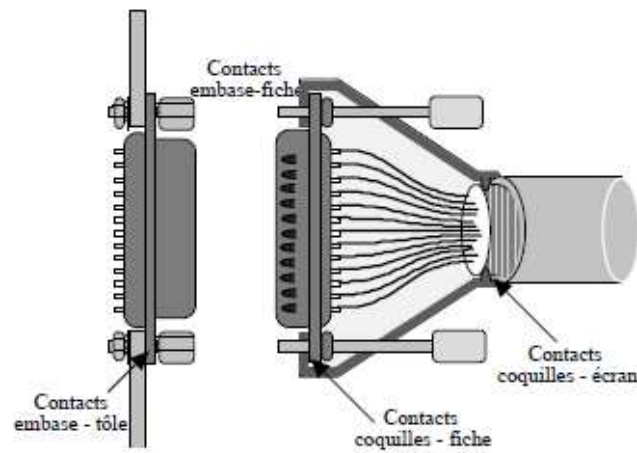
Raccordement des câbles blindés par connecteurs
